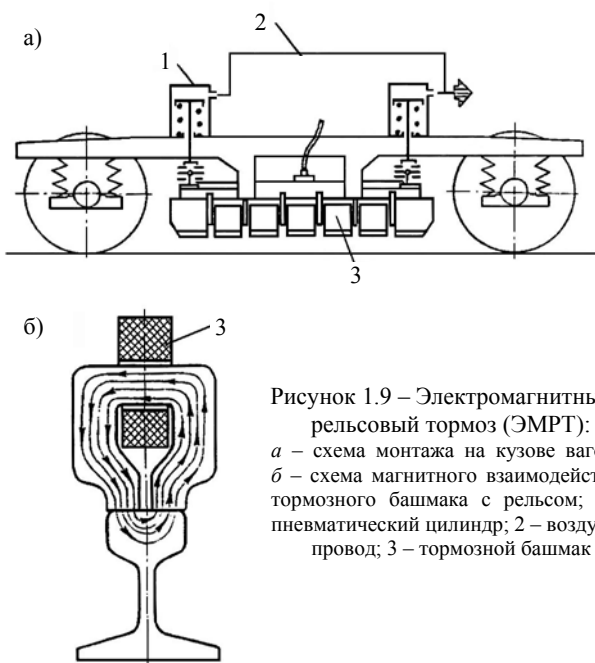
Электромагнитный рельсовый тормоз (ЭМРТ):
